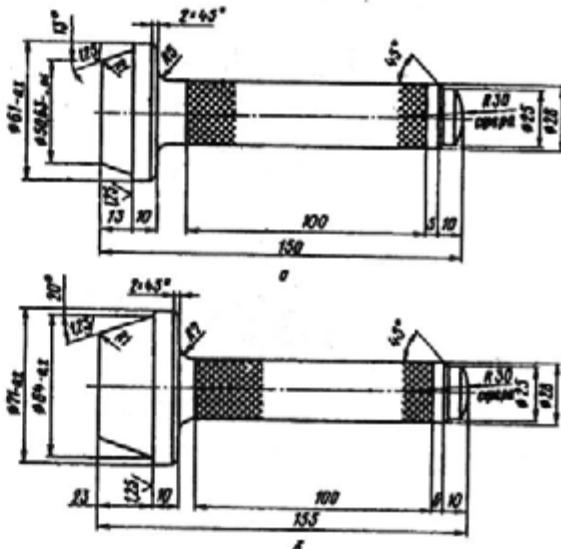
Оправки для запрессовки наружных колец подшипников ведущей шестерни главной передачи:
